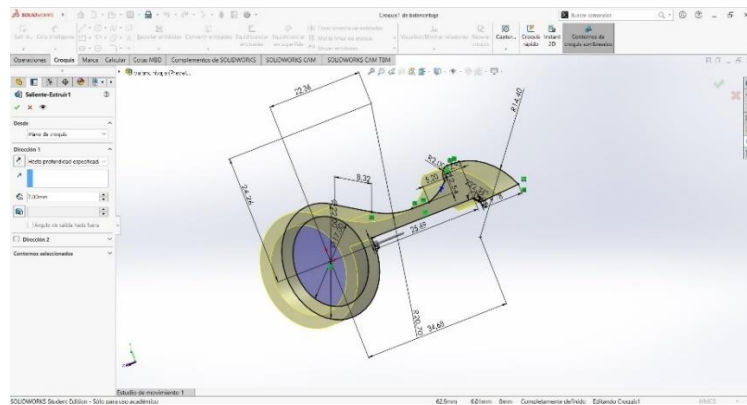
Extrusionado de croquis de Balancín 2. Fuente: SolidWorks.
